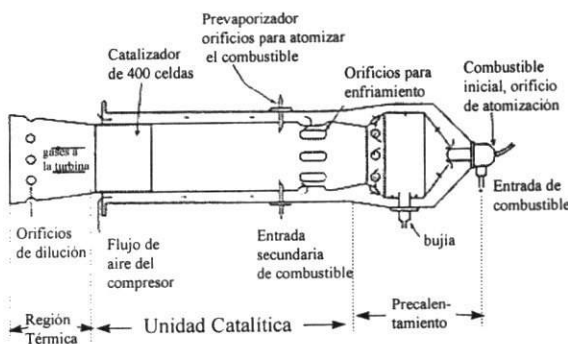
Cámara de Combustión de Johnson Matthey [2]
